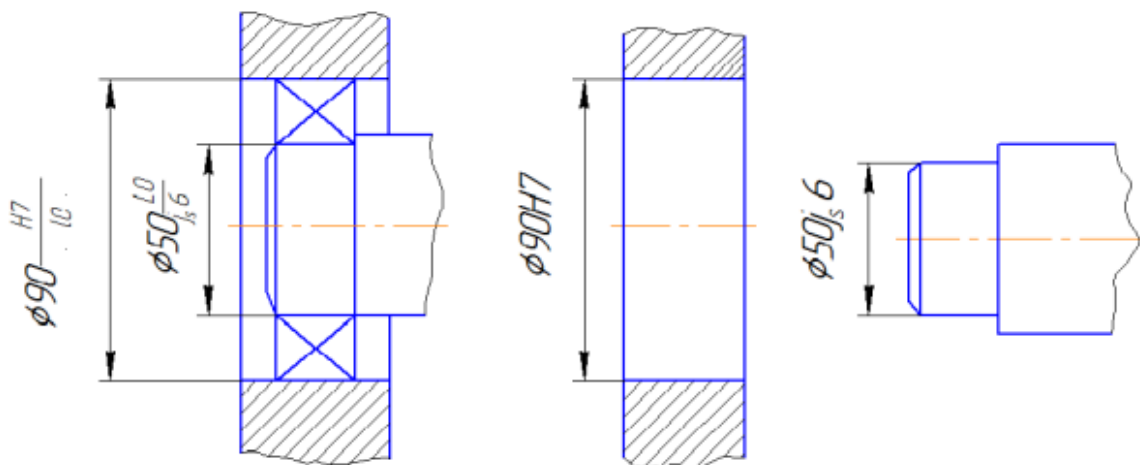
Позначення підшипникових посадок на складальних і робочих кресленнях деталей
